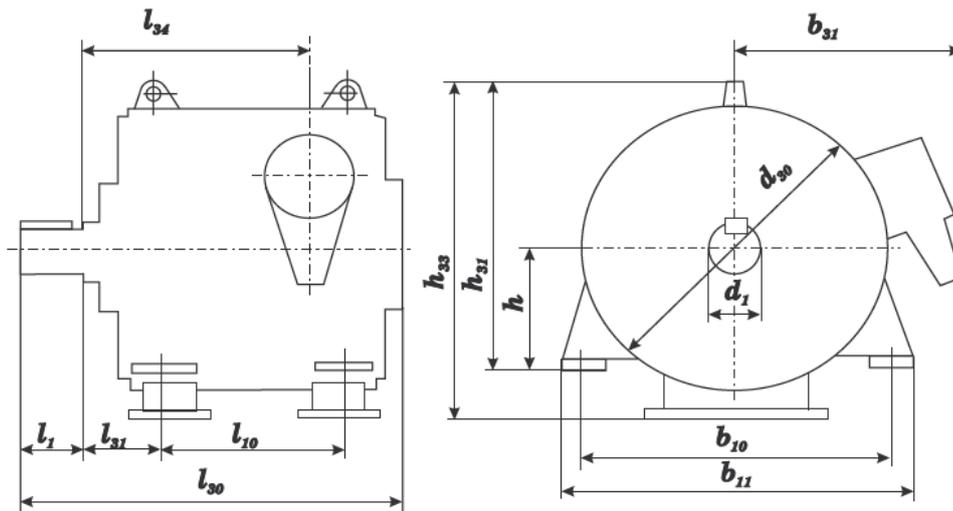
Габаритные, установочные, присоединительные размеры двигателей АНЗ-4
